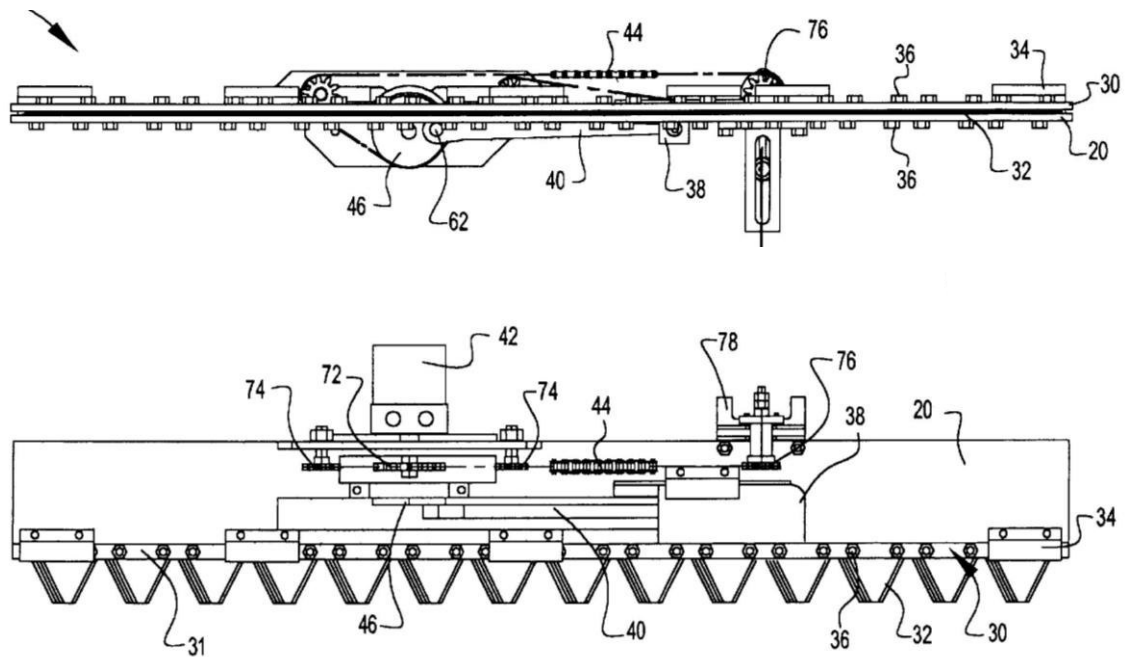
Загальний вигляд несучої плити з ріжучим механізмом
